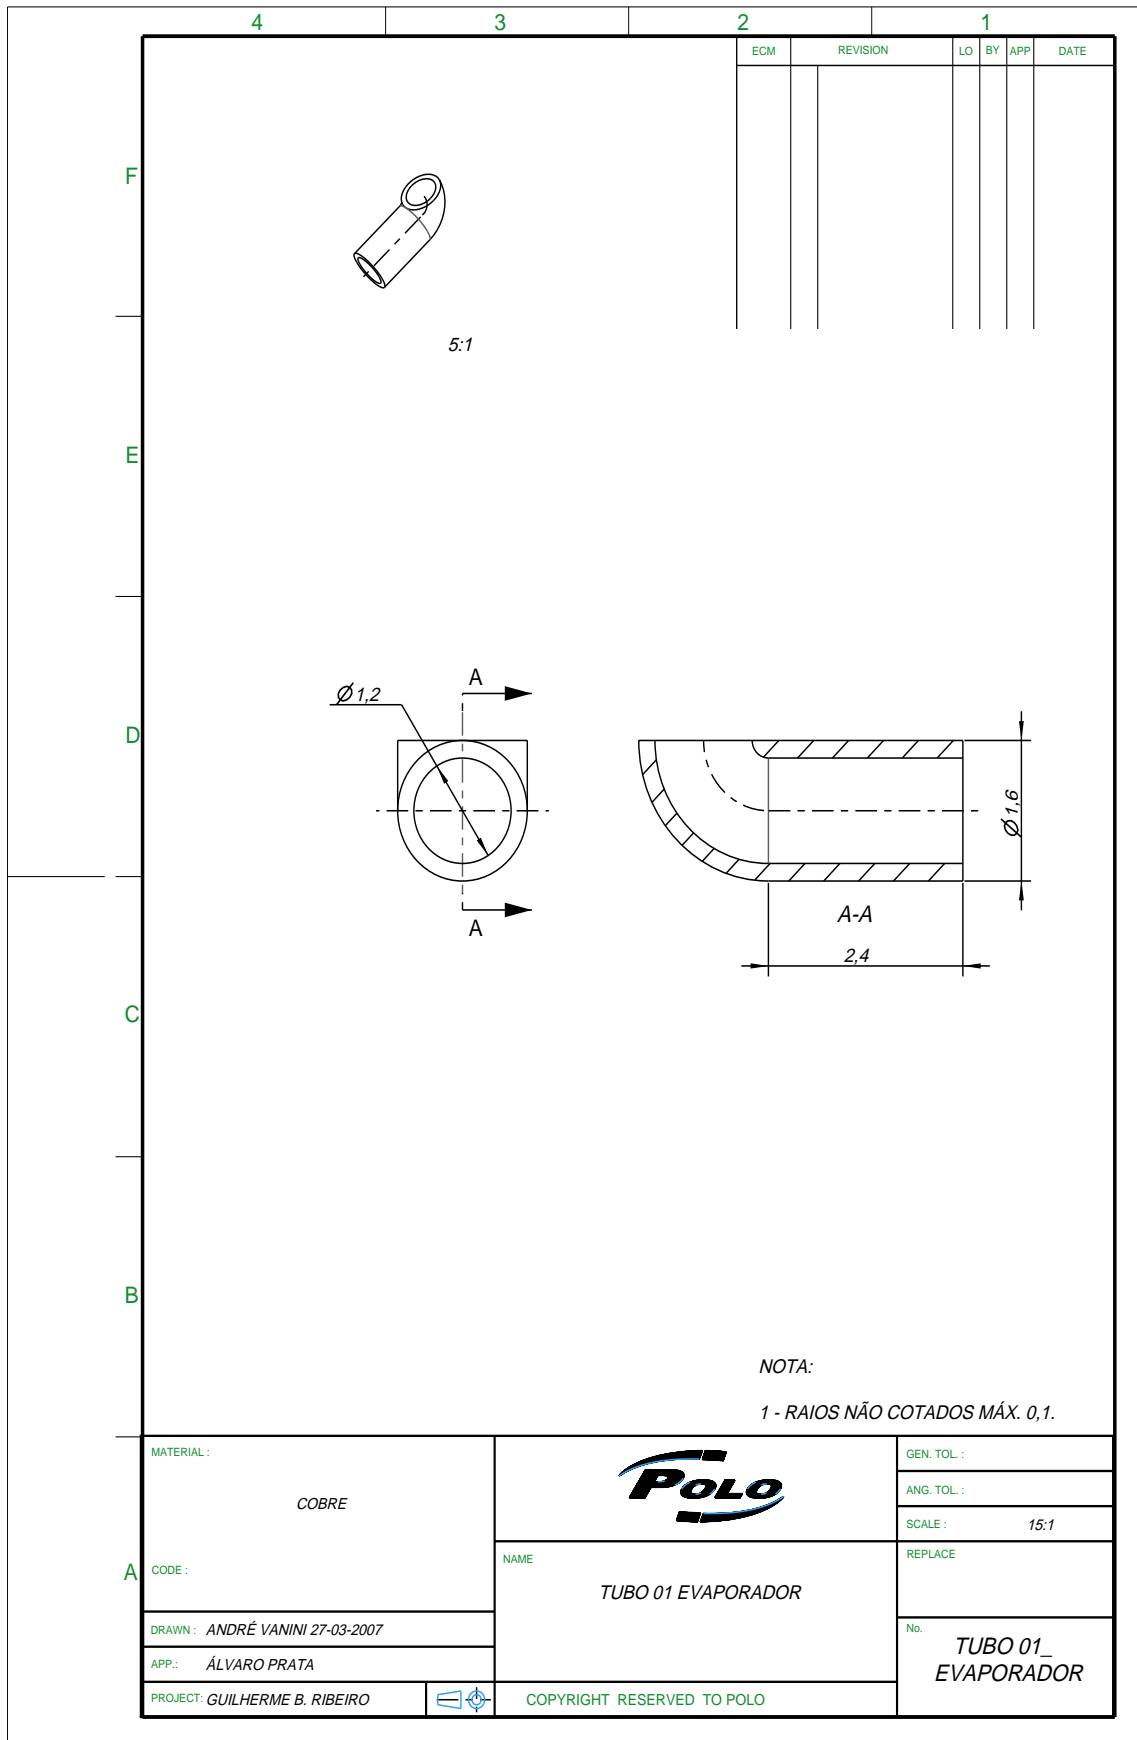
Desenho técnico do evaporador acoplado a tubos de calor - Parte VI
